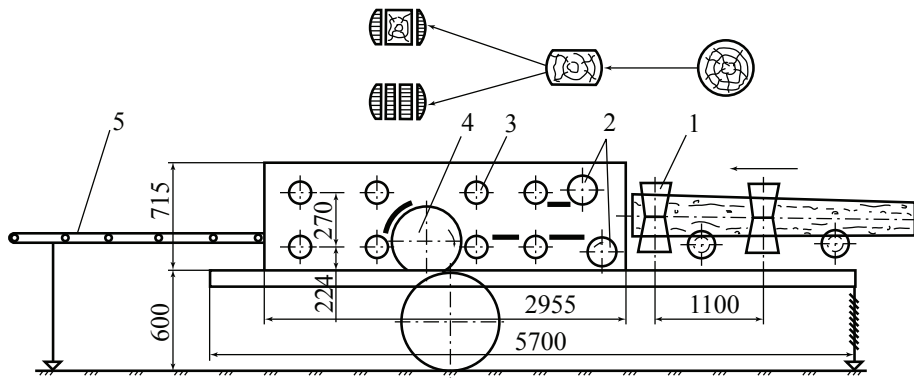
Агрегат передвижной фрезерно-пильный УПФП-1М: 1 – механизм загрузки; 2 – фрезерный блок; 3 – механизм подачи; 4 – пильный блок; 5 – роликовый стол
